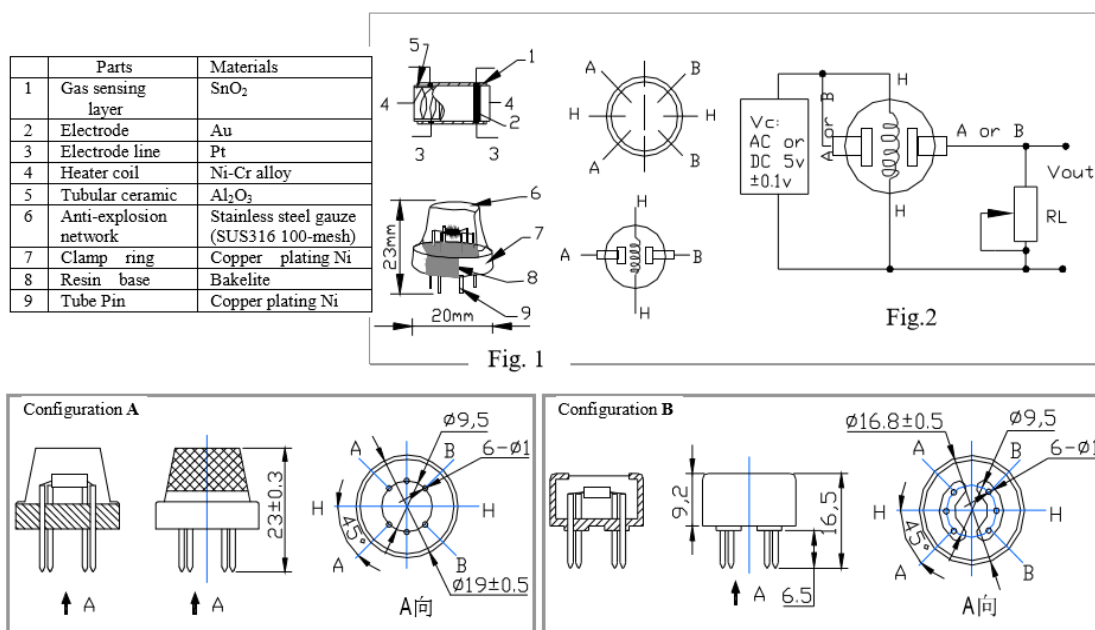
Estructura y configuración del sensor de gas equipado en el dron (Merino, 2016)
